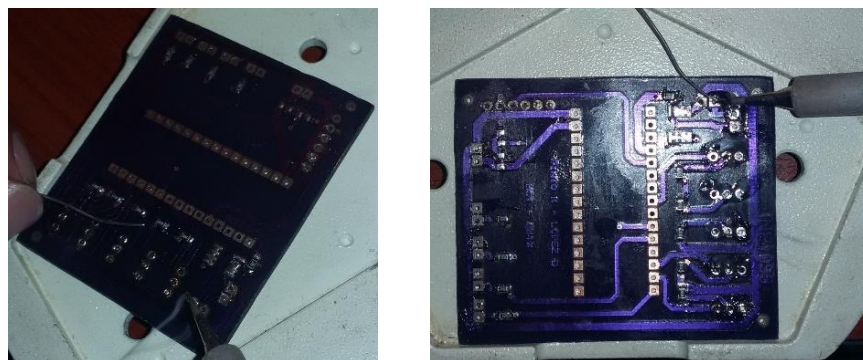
Soldado de los componentes en la placa electrónica.
